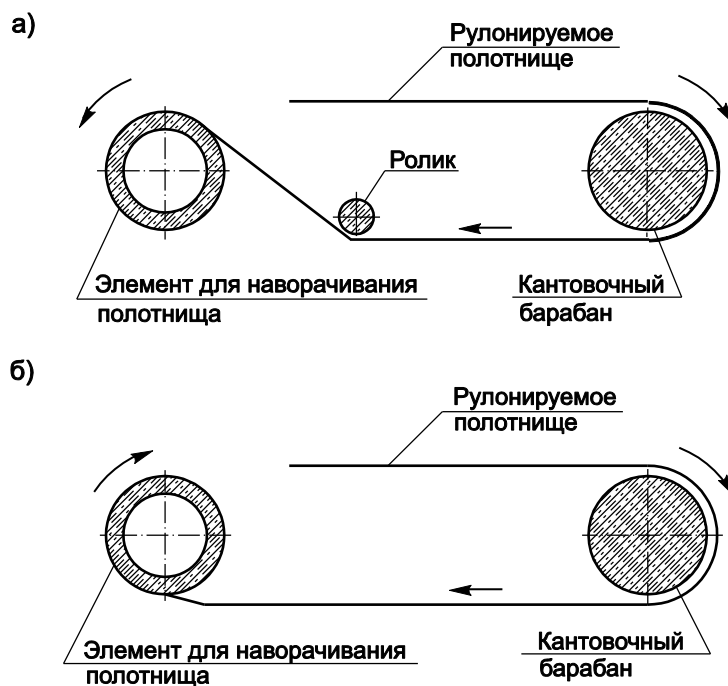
Схема установки сворачивания полотнищ:
